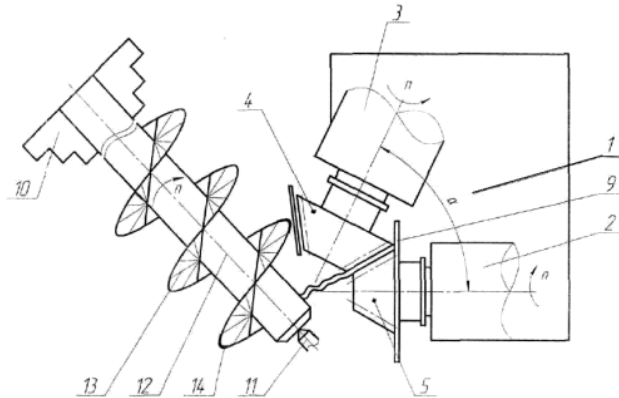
Обкатний верстат для виготовлення гвинтових гофрованих заготовок
